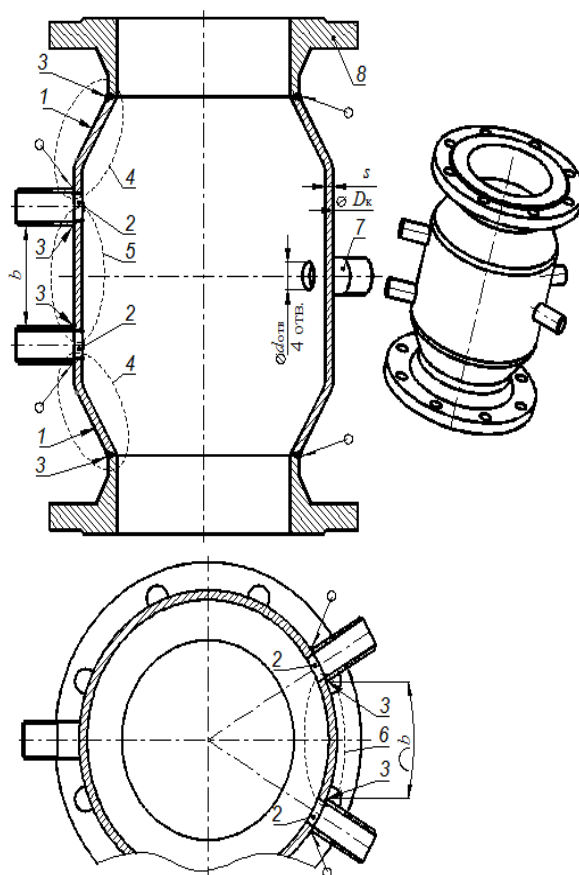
Корпус: 1 – конический переход; 2 – отверстие под штуцер; 3 – сварные швы; 4, 5, 6 – участки корпуса с повышенными остаточными напряжениями; 7 – штуцер; 8 – фланец; D_k – диаметр корпуса; s – толщина стенки корпуса; $d_{отв}$ – диаметр отверстия под штуцер; b – расстояние между наружными поверхностями соседних штуцеров
